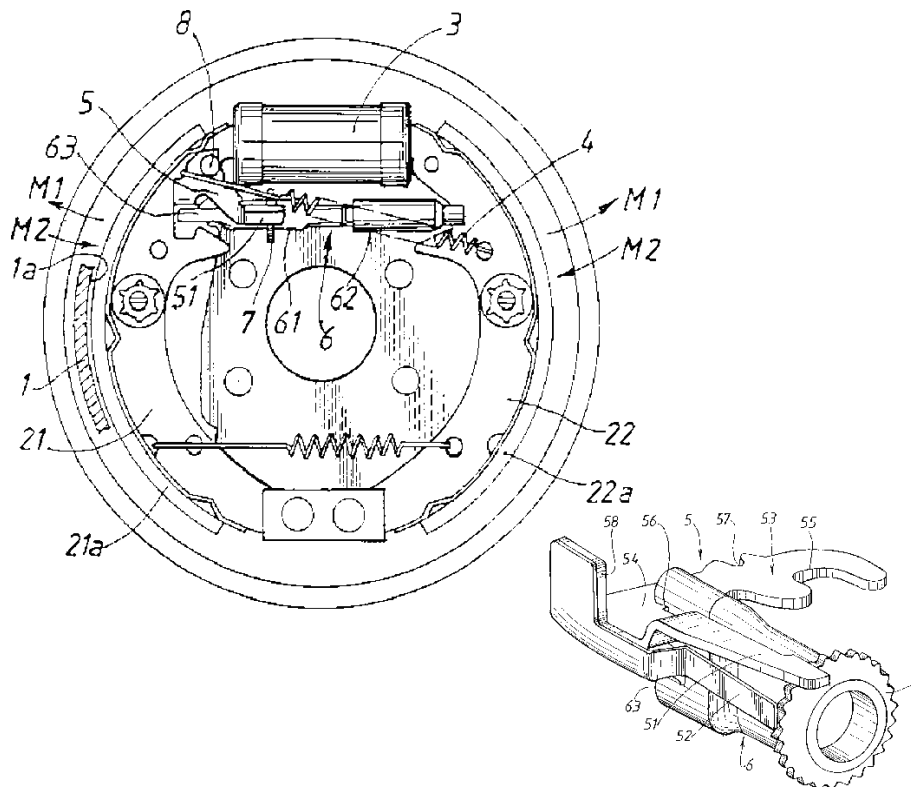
Барабанный тормоз с механизмом автоматической регулировки зазора и устройством для его избирательного отключения и блокировки.
